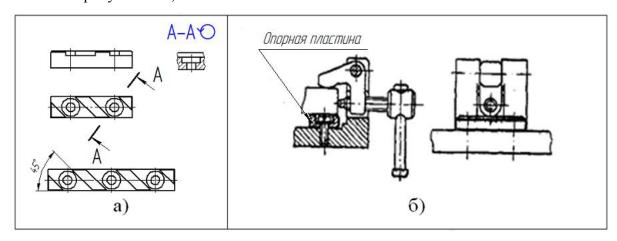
Опорные пластины: а – пластина опорная ГОСТ 4743-68; б – применение опорной пластины
